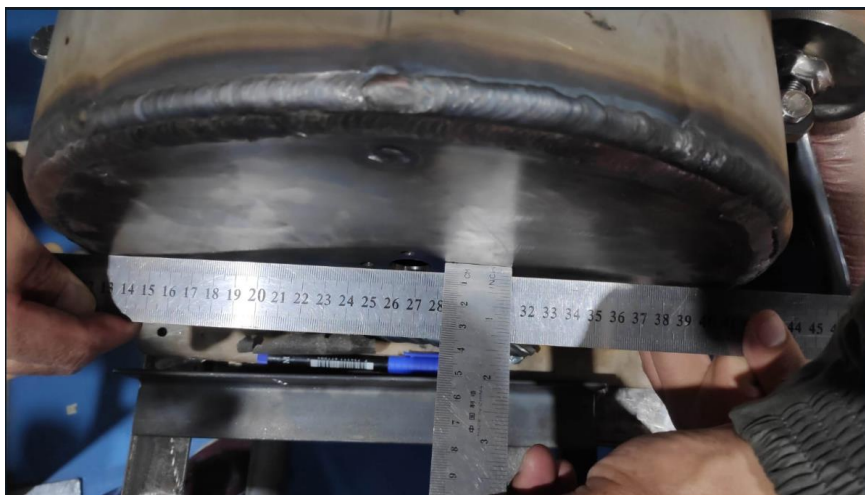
Deformación por soldadura del tope de tamiz
